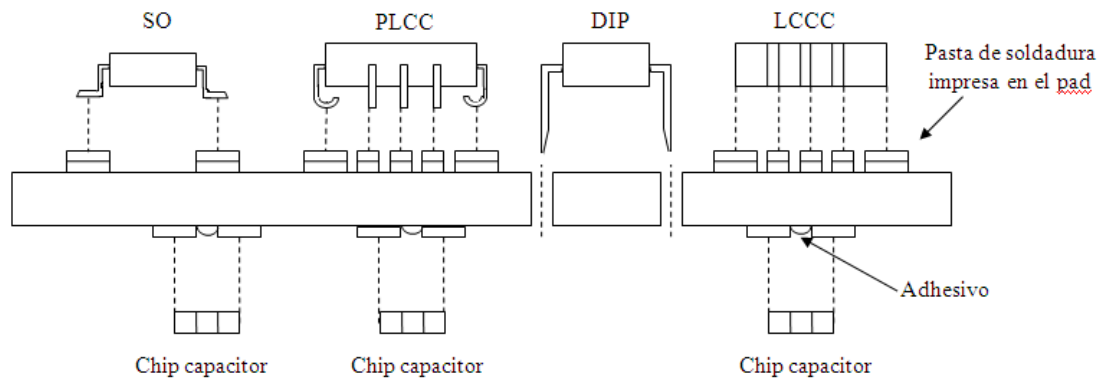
Esquemático de la placa de montaje superficial tipo II [2].
